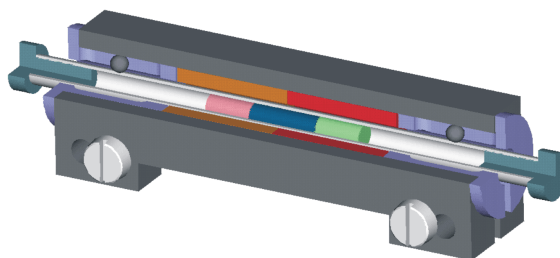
Für die integrierte Wegmessung optimierter Miniaturmotor, Baulänge 40mm
